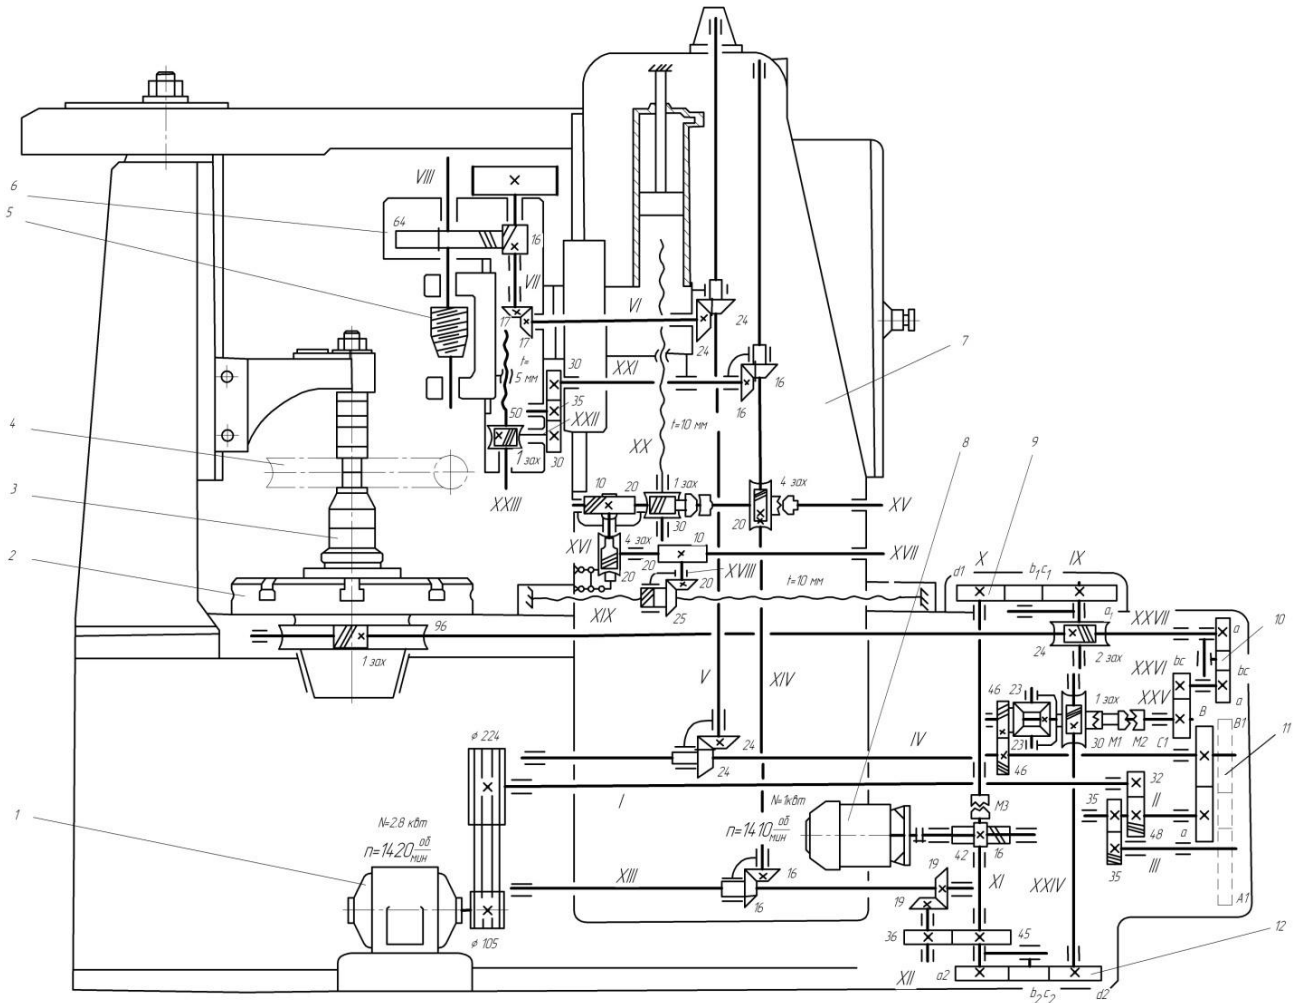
Кинематическая схема вертикально зубофрезерного станка 5Д32
